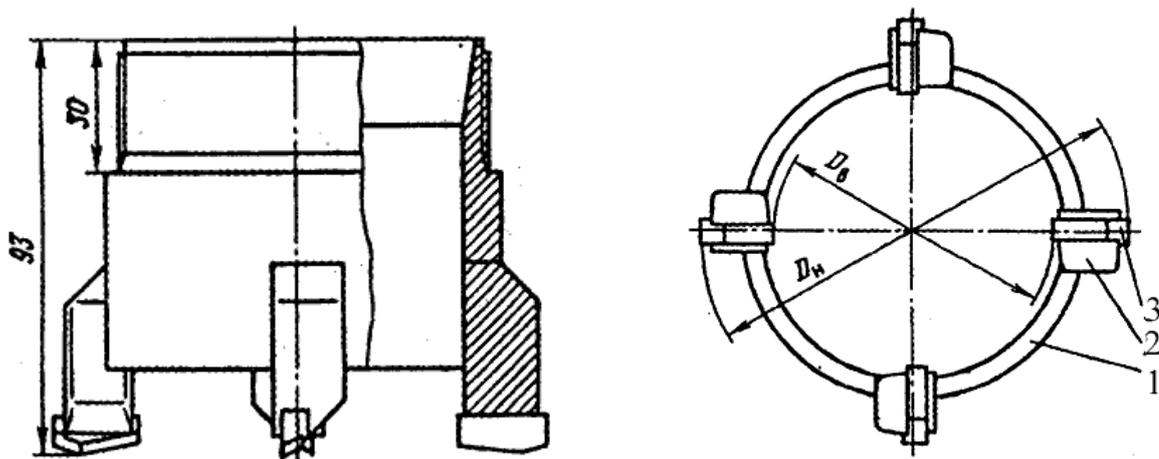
Серийная твердосплавная коронка типа М6
